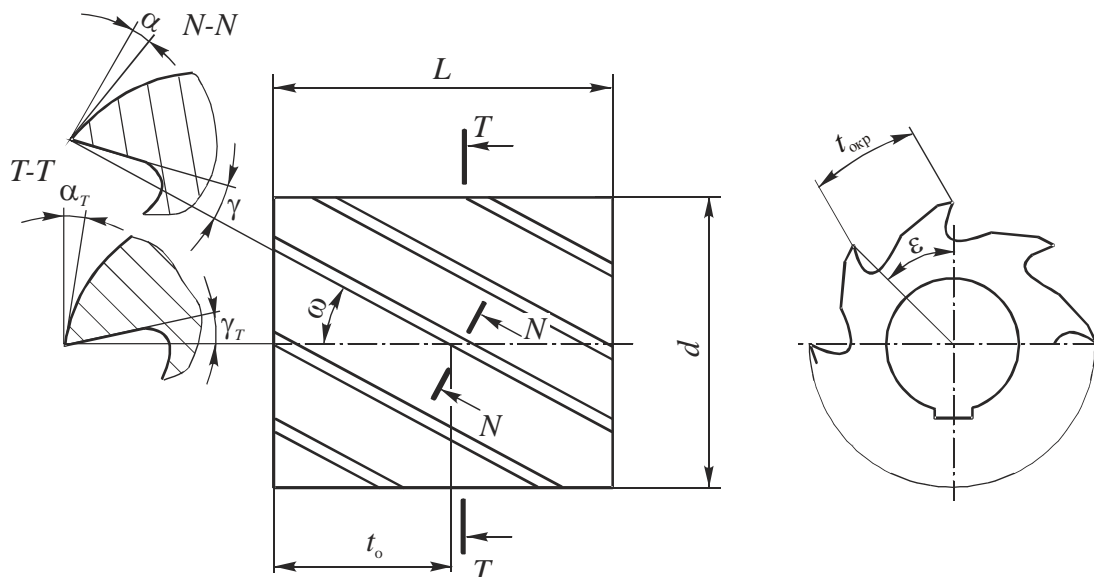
Конструктивные и геометрические параметры цилиндрической фрезы
